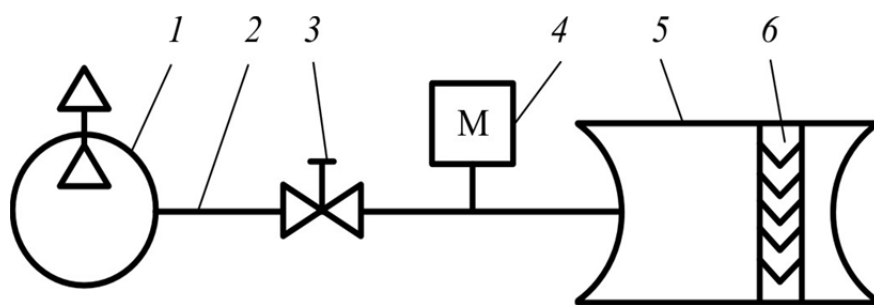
Схема контролю способом диференціального манометричного перетворення: 1 — вакуумний насос; 2 — магістральний трубопровід; 3 — вентиль; 4 — диференціальний манометричний перетворювач; 5 — контрольований виріб; 6 — зварний шов
